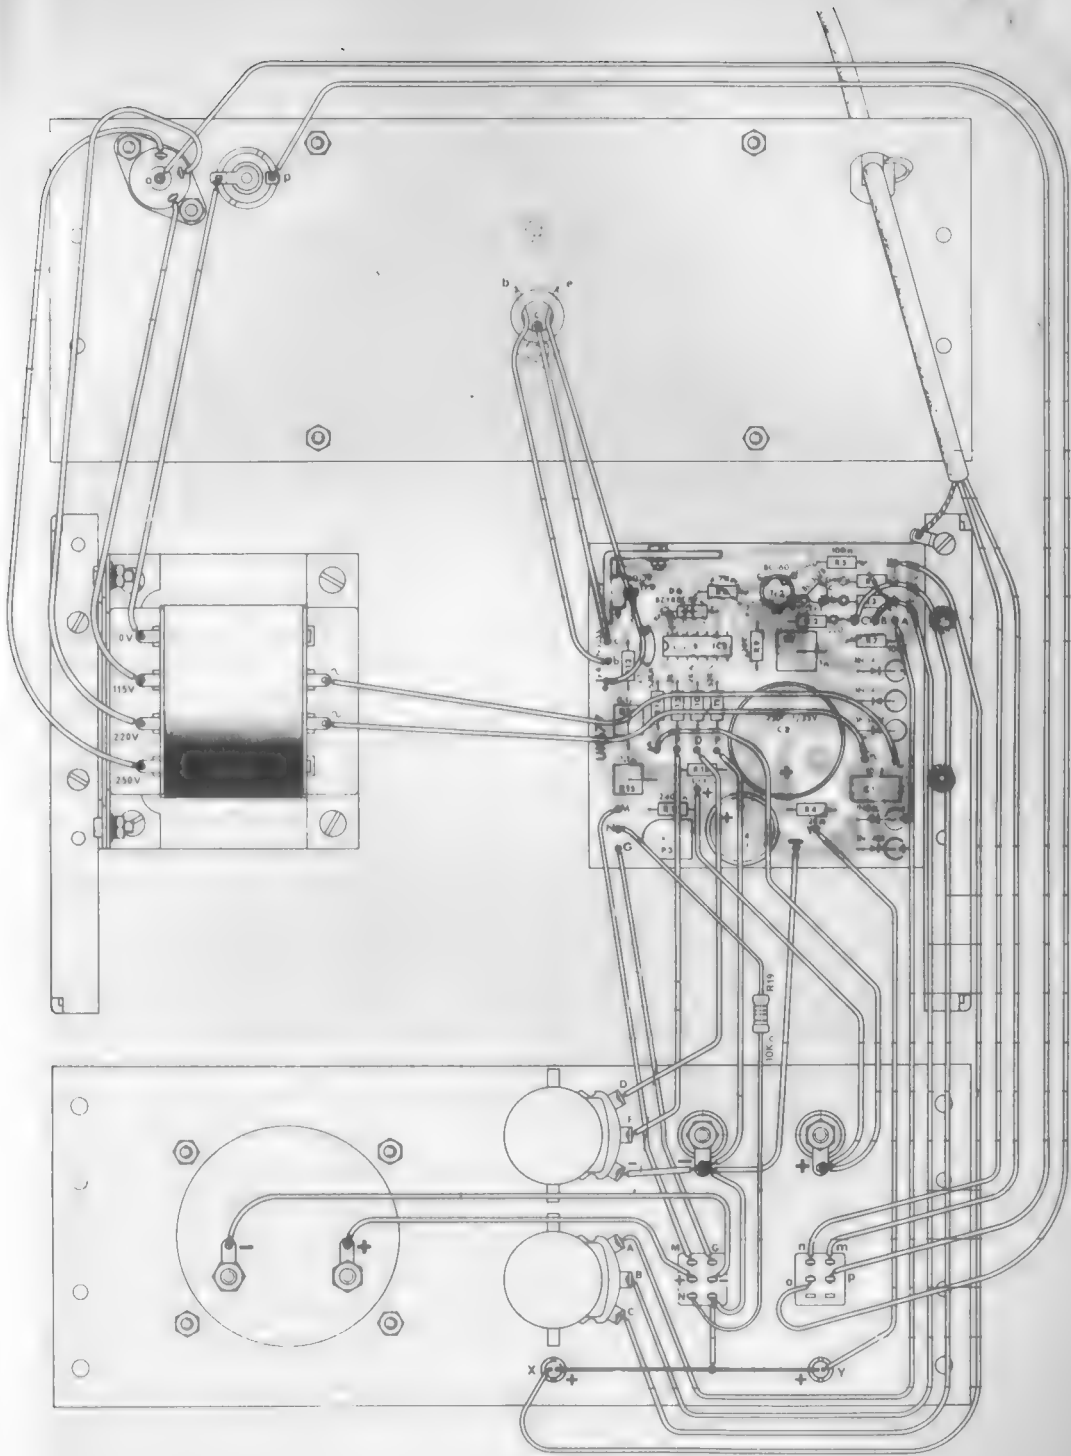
Montaggio di tutte le parti necessarie a completare il pannello frontale.
